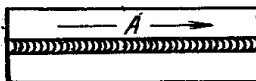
Сварка коротких швов на проход (А — общее направление сварки).
